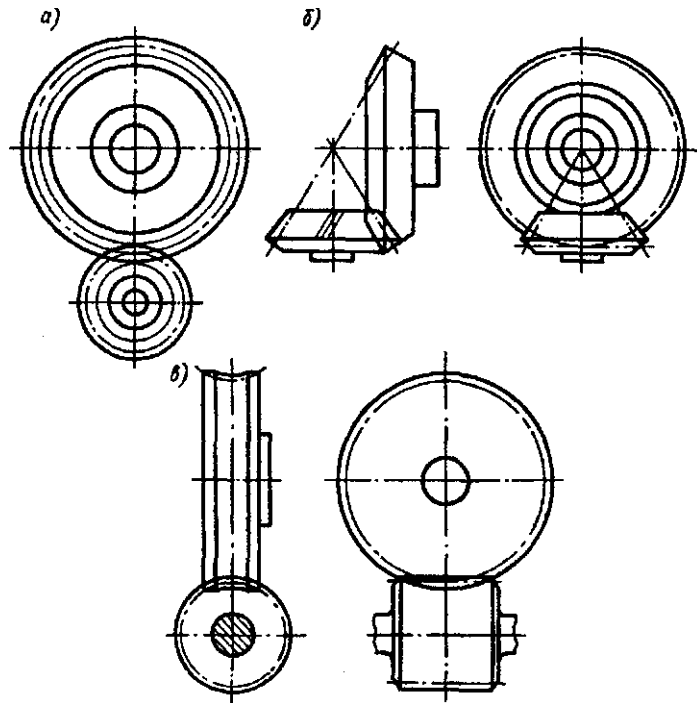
Зацепления: *a* — зубчатое цилиндрическое; *б* — зубчатое коническое; *в* — червячное
